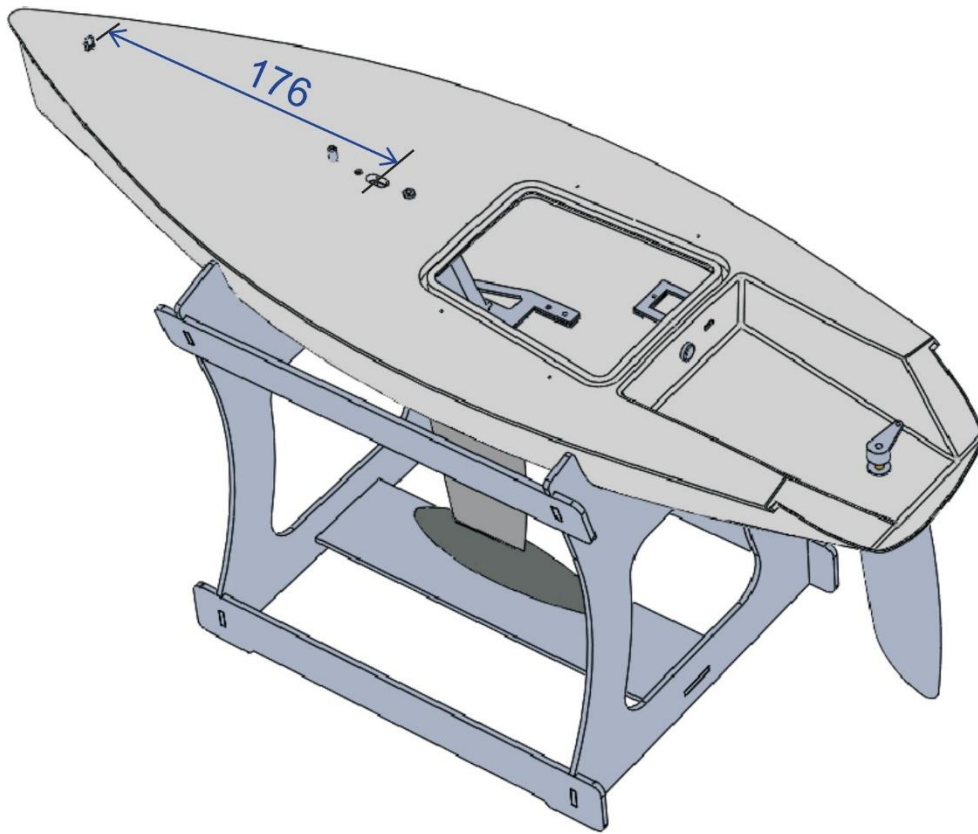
Fixation de la fixation de la bôme de foc sur les coques 2014.v2
